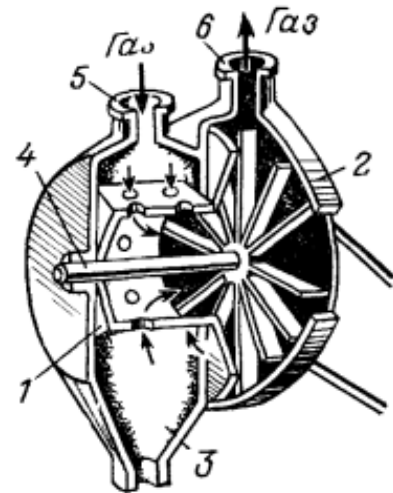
Відцентровий пиловловлювач конструкції Розенкранца та Пречистенського: 1 – перфорований барабан; 2 – вентилятор; 3 – корпус; 4 – вал; 5, 6 – патрубки
